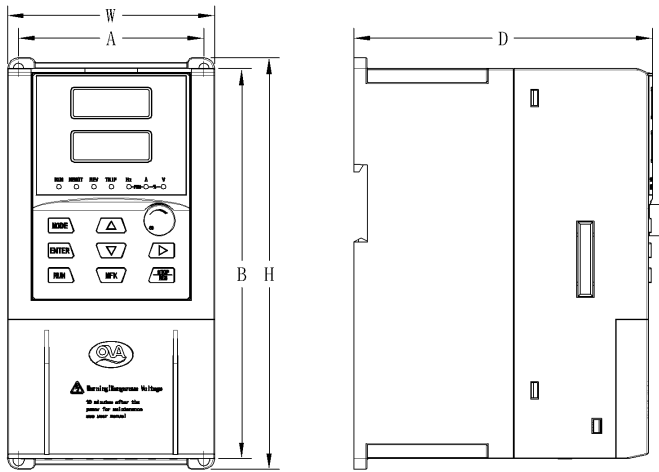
EM600系列塑胶机箱结构外型尺寸及安装尺寸示意图
